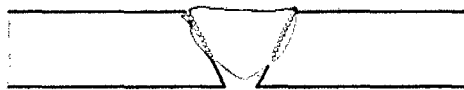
Penetración incompleta. (Referencia Oxagasa, 2014, Manual del Soldador, El Salvador ,88P).
